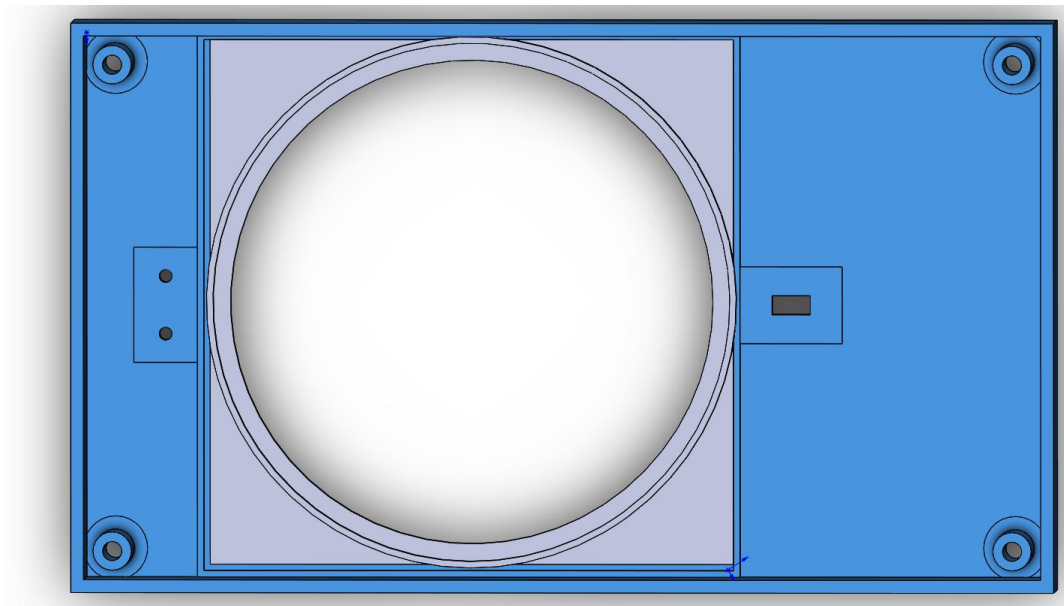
Нижня частина корпусу, вид зсередини
